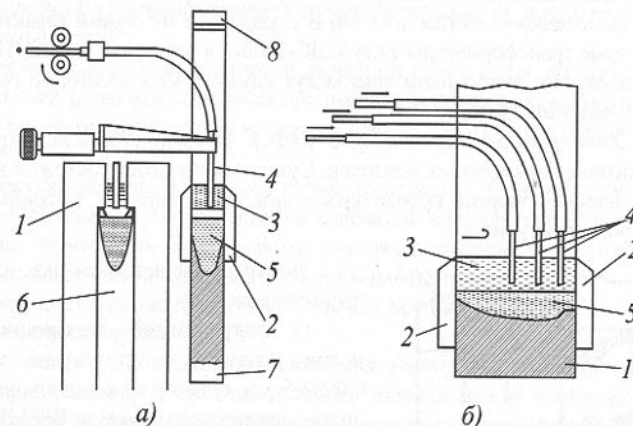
Схема электрошлаковой сварки
